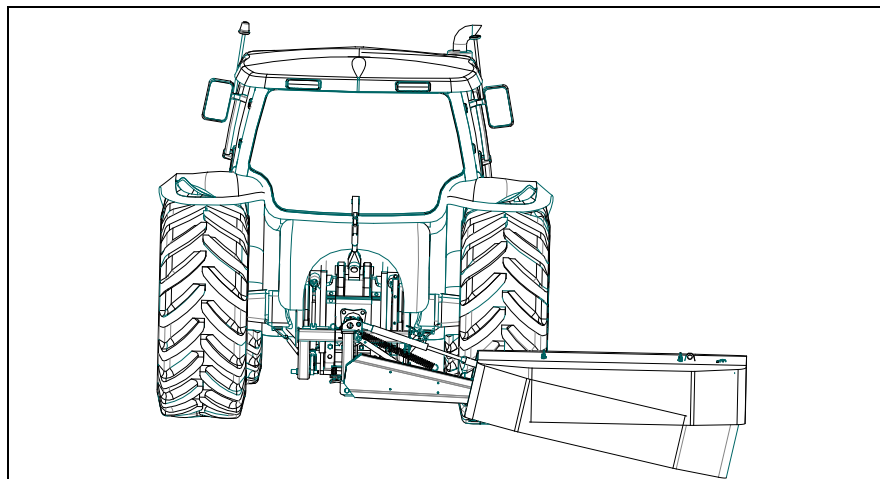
Рабочий диапазон косилки (рабочий диапазон режущего аппарата - 8°; рабочий диапазон балки - 0÷12°)
